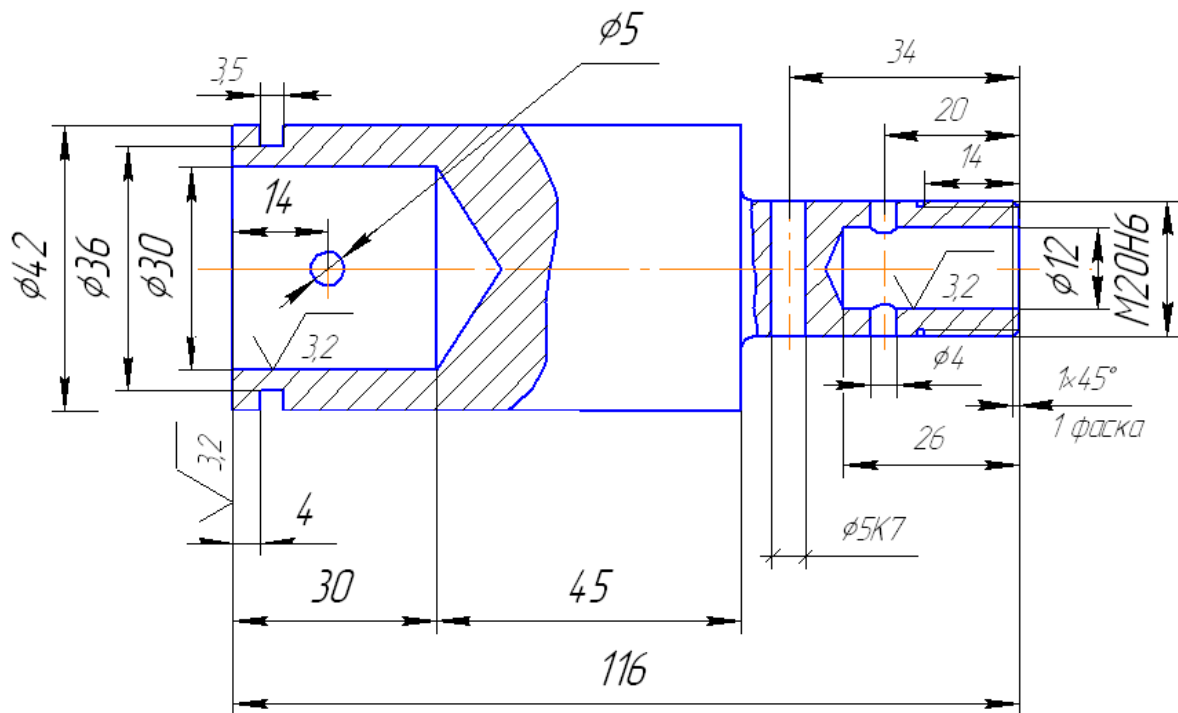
Схема до розрахунку деталі вал-втулка.
